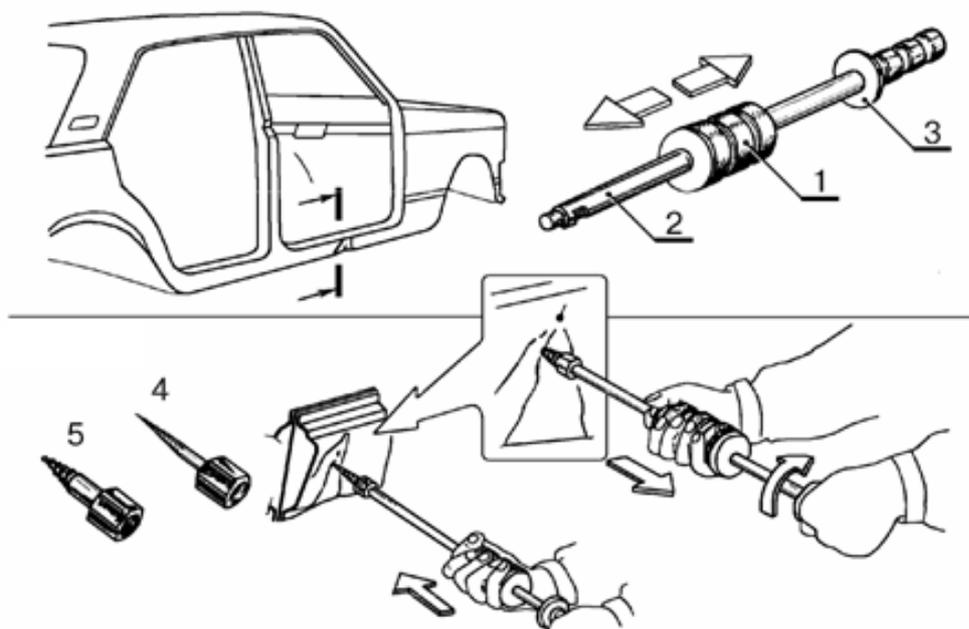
Исправление вмятин приспособлением ударного типа:
